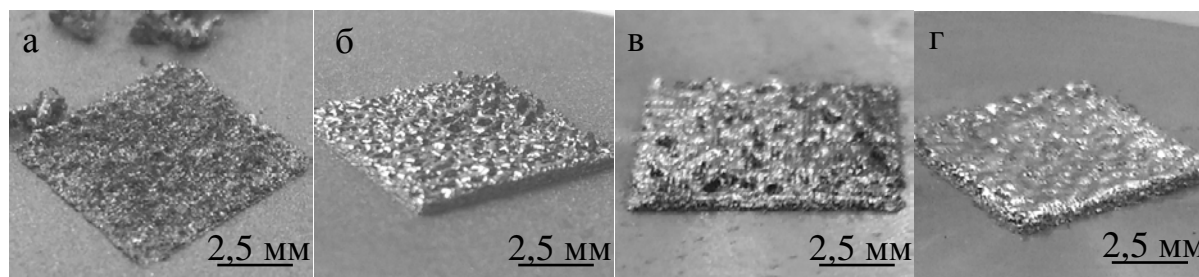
Фотографии образцов, полученных СЛС на установке «Луч»: а – образец № 1; б – образец № 2; в – образец № 3; г – образец № 4
